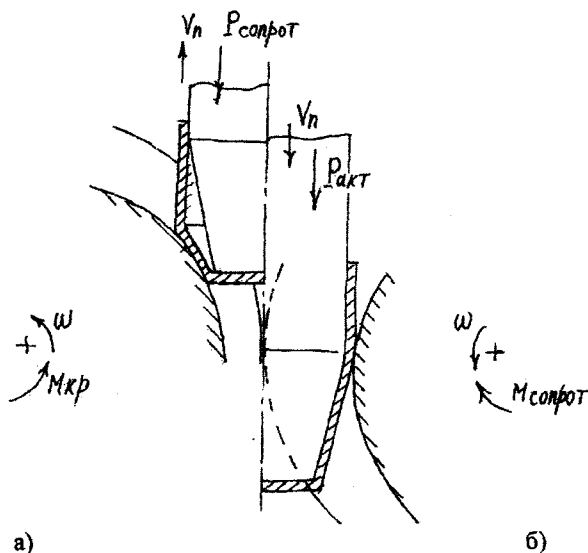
Схема вытяжки рассматриваемой детали через вальцы
